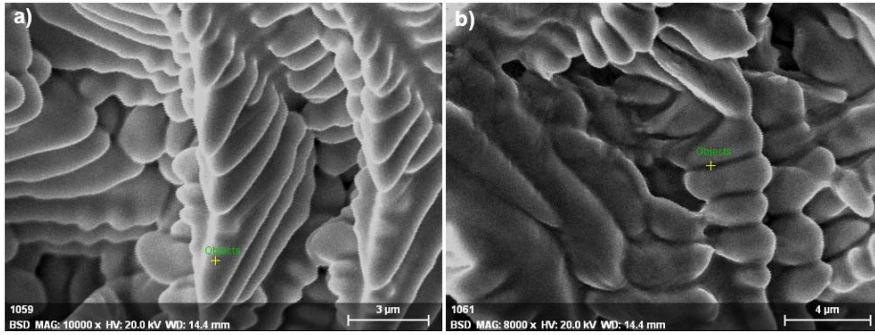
8 kA ile kaynak edilen numuneye ait çekme testi sonrasındaki SEM kırılma yüzeyi görüntüleri (SEM fracture surfaces after tensile testing of the sample welded with 8 kA)
